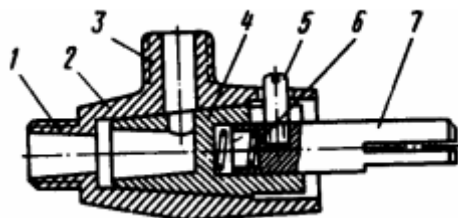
Унифицированный пробковый кран газовой плиты: 1 – штуцер для присоединения к газопроводу; 2 – корпус; 3 – штуцер для присоединения к коллектору; 4 – пробка; 5 – стопорный винт; 6 – пружина; 7 – стержень
